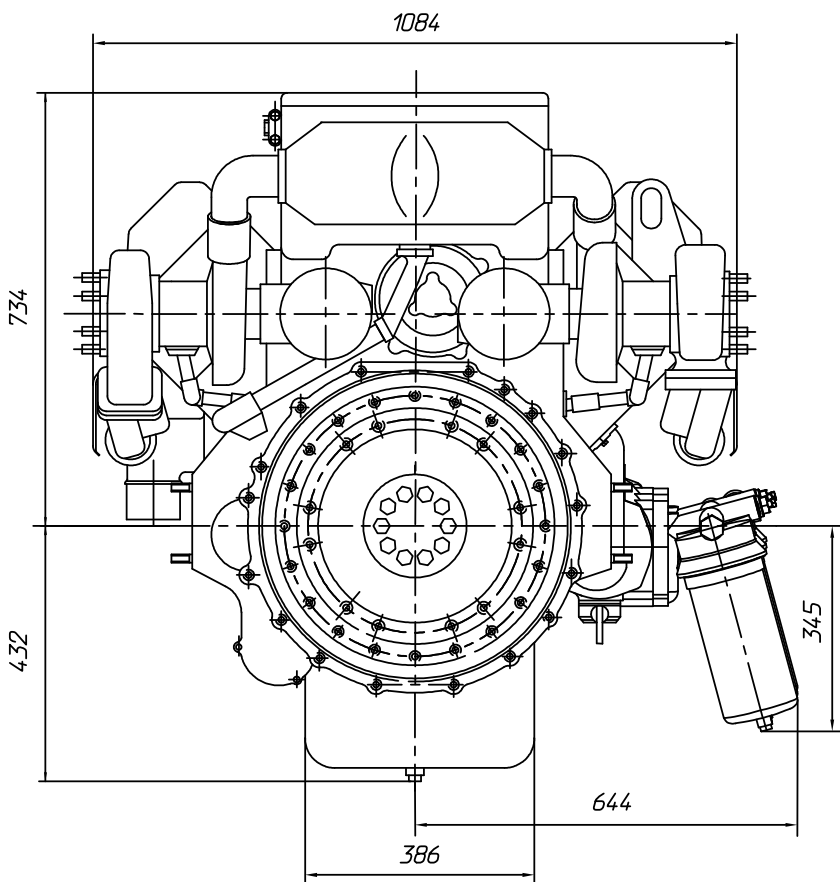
Габаритные размеры двигателя (вид сзади)
